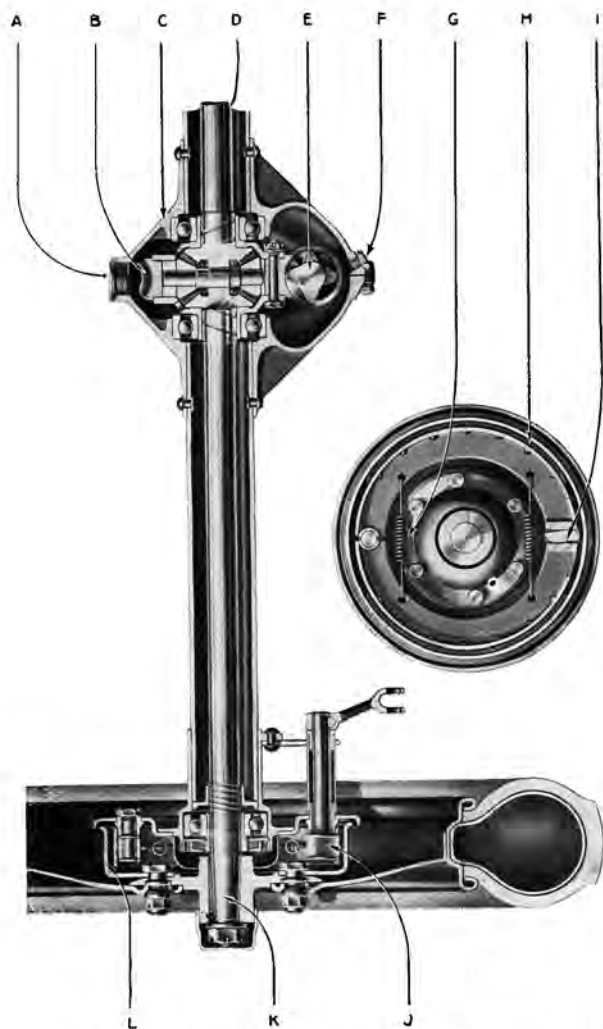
Coupe du pont arrière et vue d'un frein.
